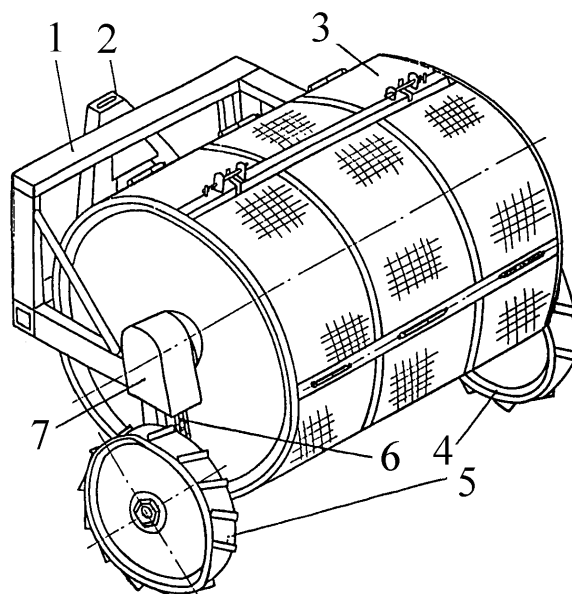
Мульчирователь МСН-0,75: 1 – рама; 2 – автосцепка; 3 – люк барабана; 4 – правое опорное колесо; 5 – левое приводное колесо; 6 – цепная передача; 7 – защитный кожух
